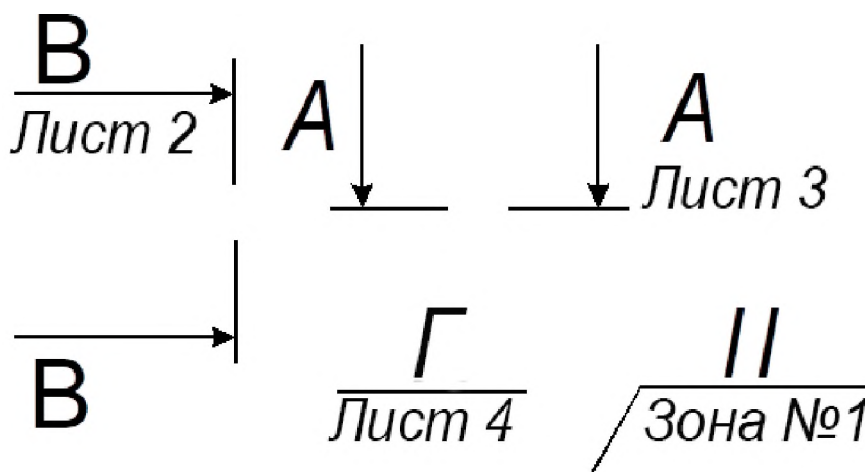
Обозначение дополнительных изображений на чертежах
